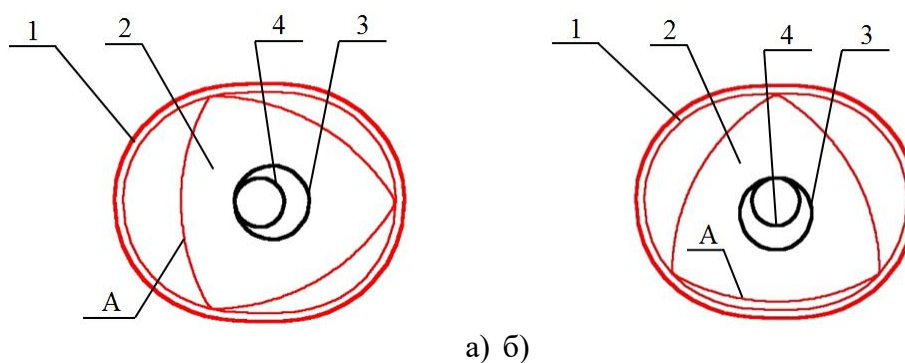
Положення робочих органів планетарно-роторного компресора:
